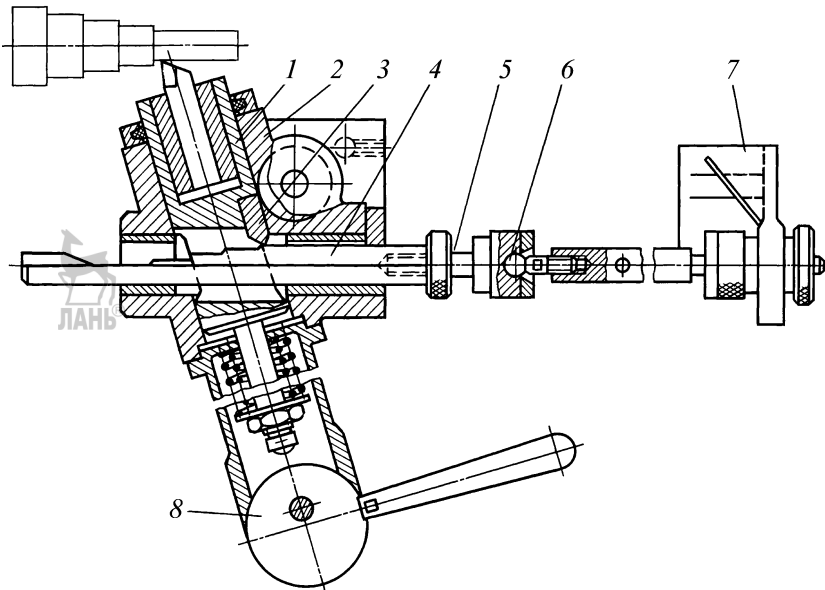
Приспособление для полуавтоматической обработки ступенчатых валов:
